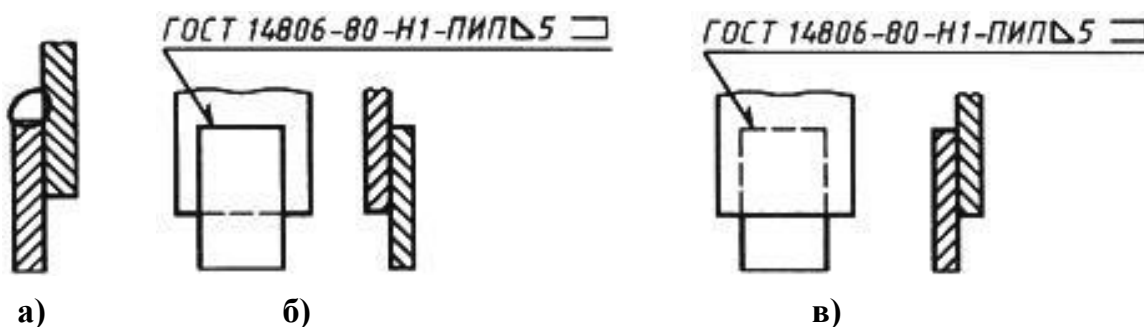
Пример обозначения сварного шва [5]: а – форма поперечного сечения шва; б – обозначение с лицевой стороны; в – обозначение с оборотной стороны
